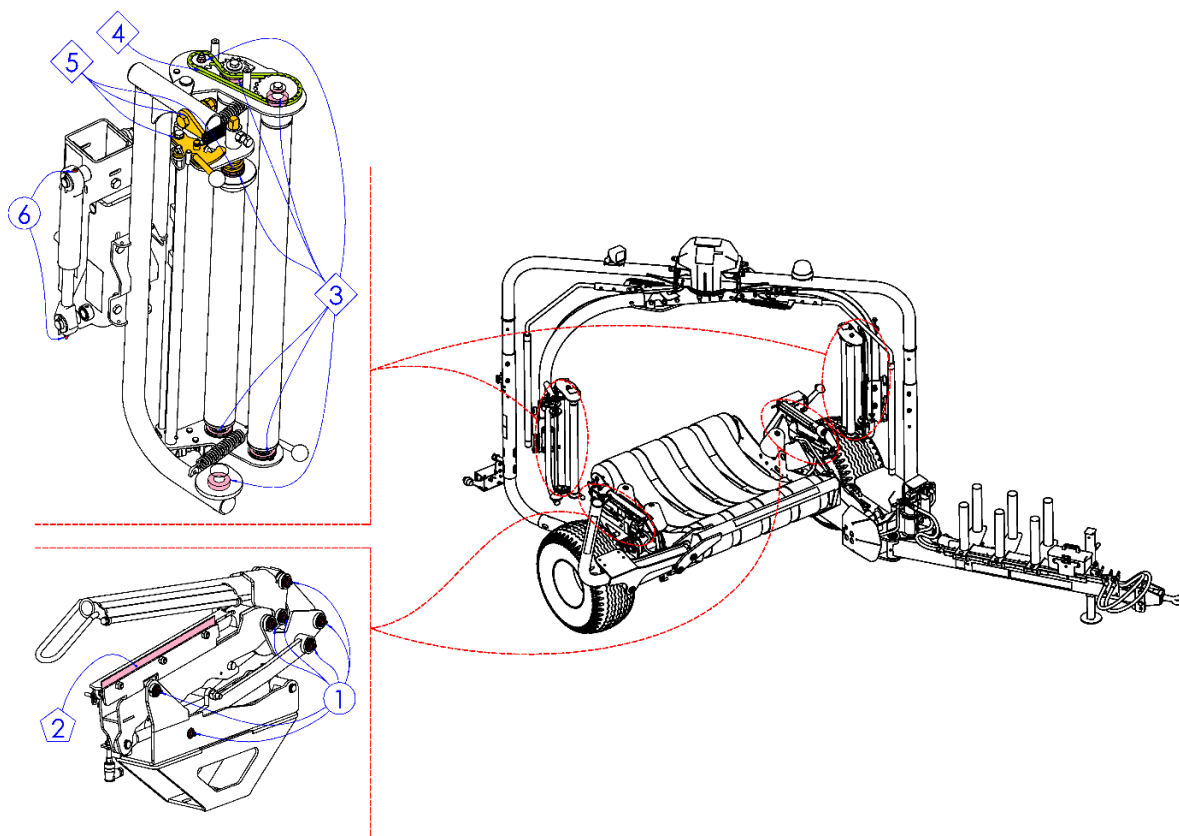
Точки смазывания механизма обрезки пленки и подавателя пленки: 1 – смазочные ниппели подшипников скольжения механизма обрезки; 2 – обрезающий нож 3 – подшипники подавателя; 4 – приводная цепь передачи подавателя; 5 – верхний прижим рулона пленки; 6 - смазочные ниппели подшипников цилиндра механизма подачи
